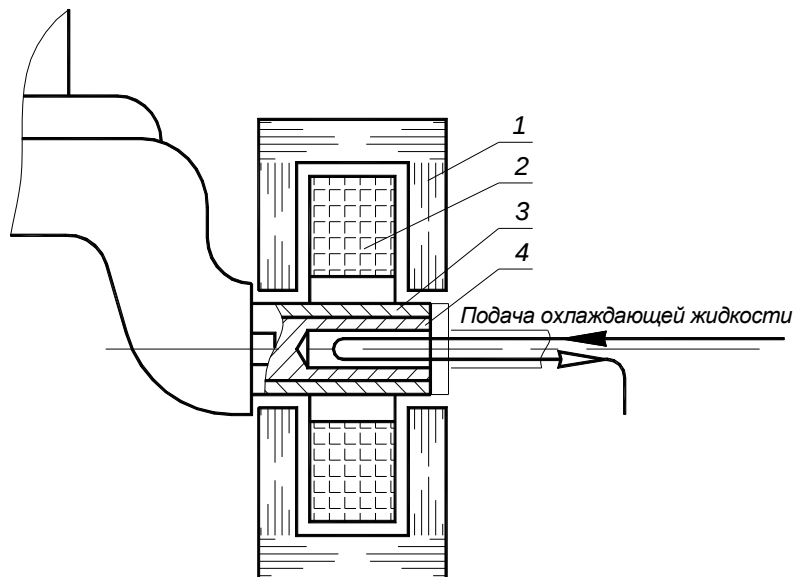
Схема установки для съема втулки с карданного вала:
